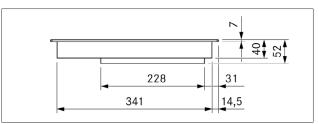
Dimensões do aparelho PKI3, vista dianteira
